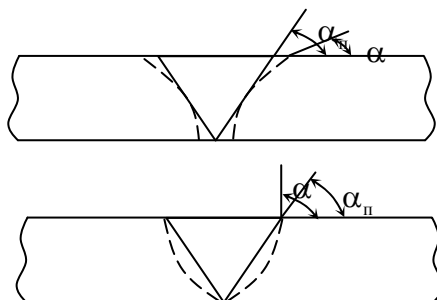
Оплавление кромок в процессе сварки:
